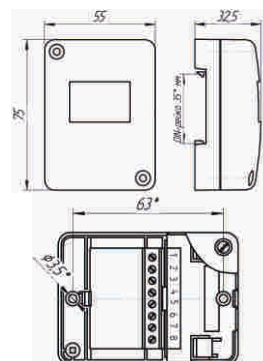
Габаритные и установочные размеры контроллера считывателя.
